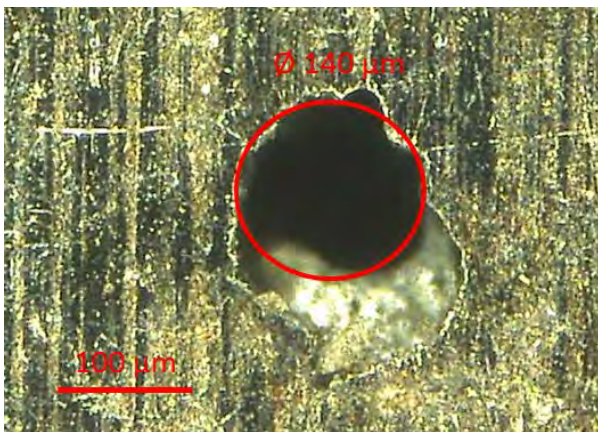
Austrittsloch einer Bohrung in 5 mm Werkzeugstahl 1.2379.
